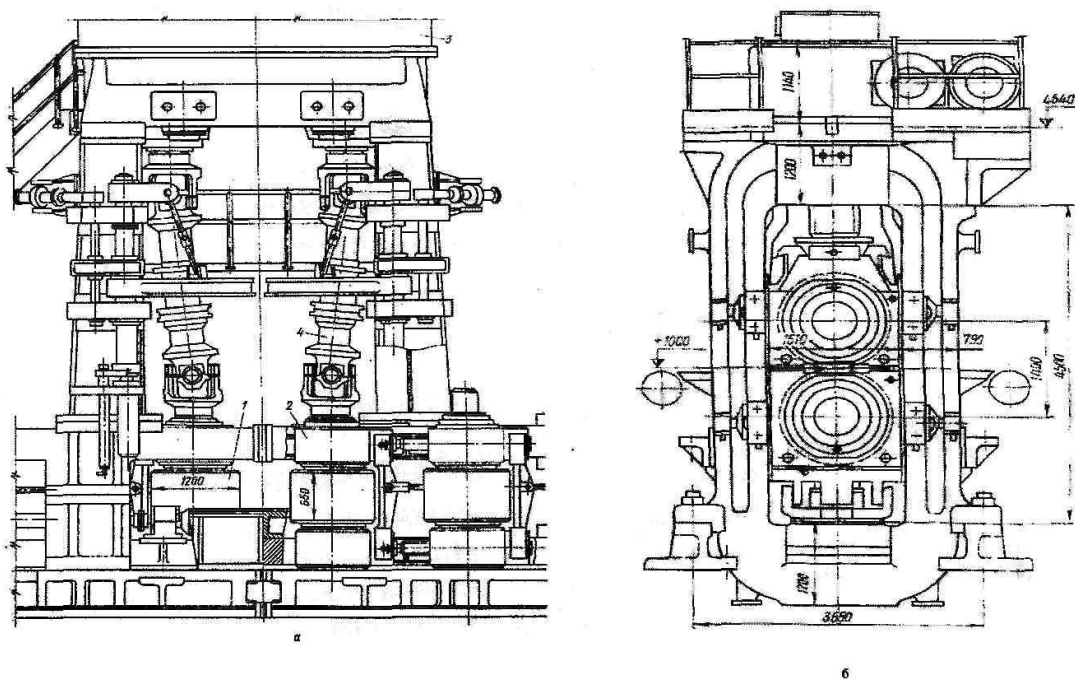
Черновой двухвалковый окалиноломатель с вертикальными валками 1200x650 мм (а) и черновая двухвалковая клетка с горизонтальными валками 1400x2000 мм (б)
